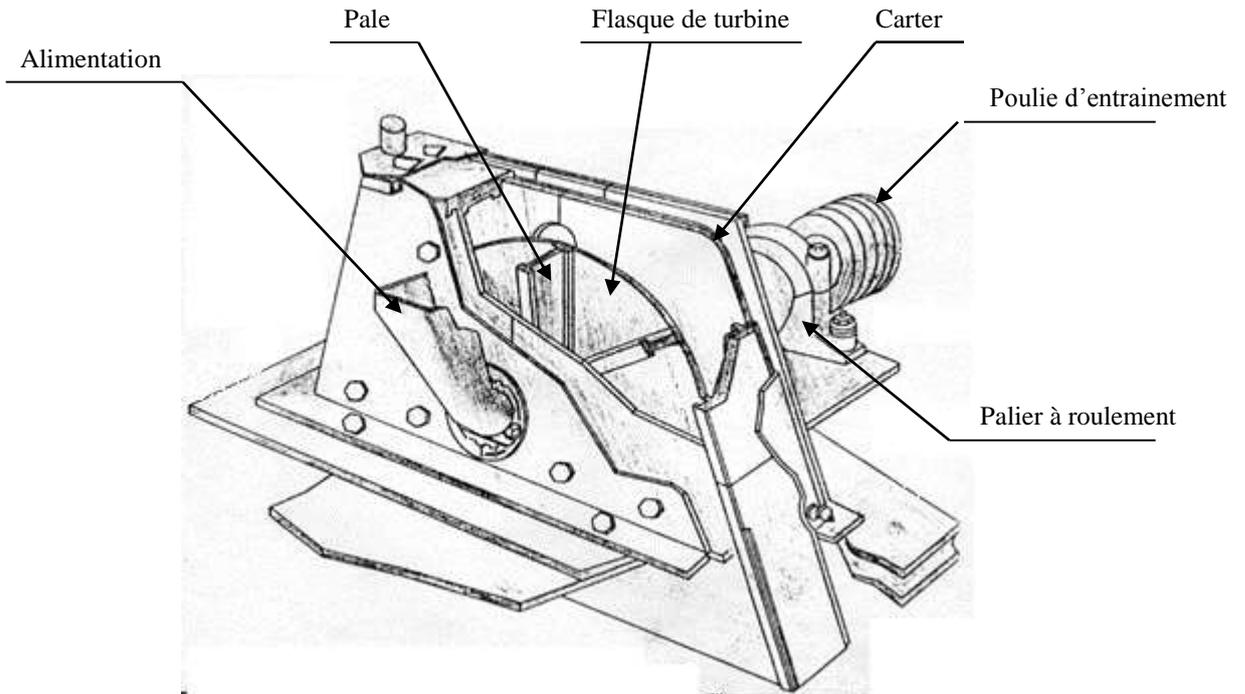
Vue extérieure en perspective de l'ensemble turbine [09]
